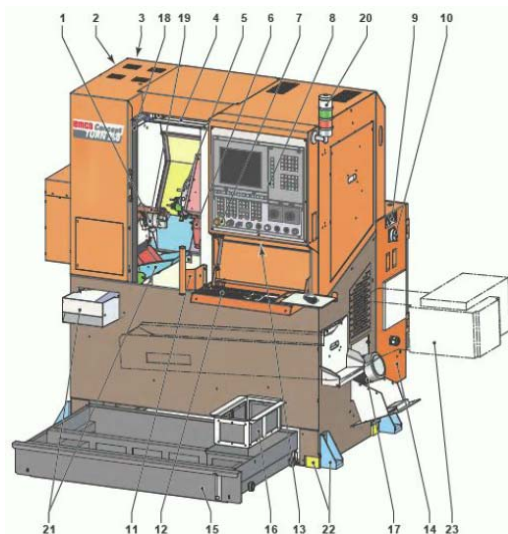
Общий вид токарного станка *Emco Concept Turn 250
